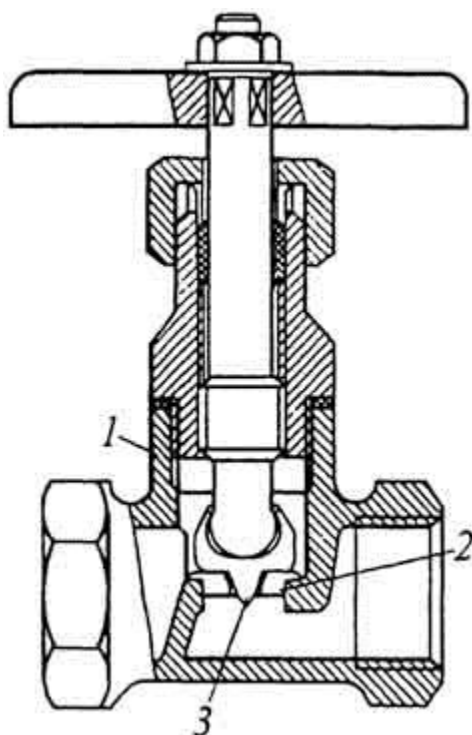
Кран регулирующий с дросселирующим устройством: 1 - сборка корпуса муфтового запорного вентиля с крышкой, шпинделем, накидной гайкой и рукояткой; 2 - калиброванная диафрагма; 3 - запорно-регулирующий клапан
